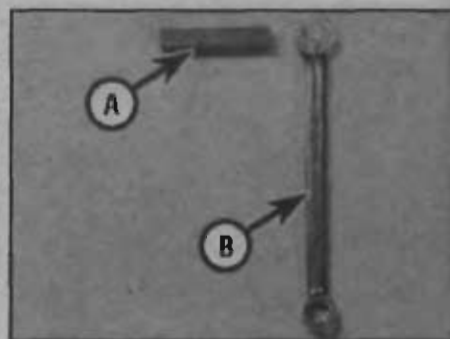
Квадратный стержень (А) и гаечный ключ (В), используемые для поворота шкива механизма натяжения зубчатого ремня
